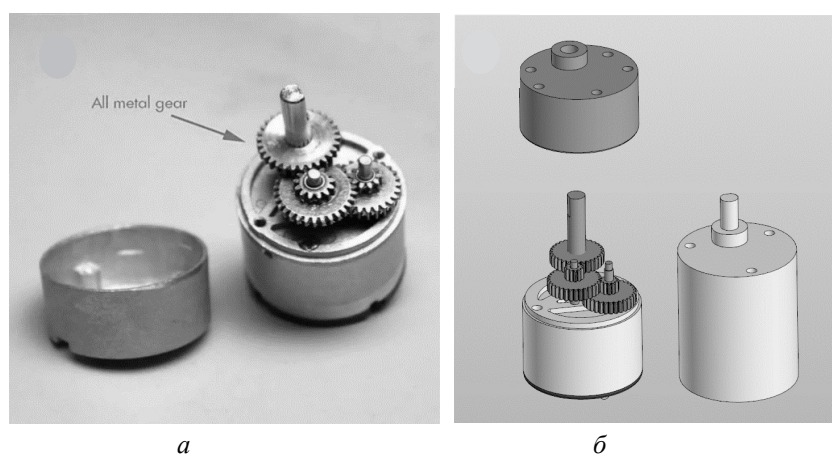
Внутреннее строение редуктора двигателя 33GB-520-18.7:
